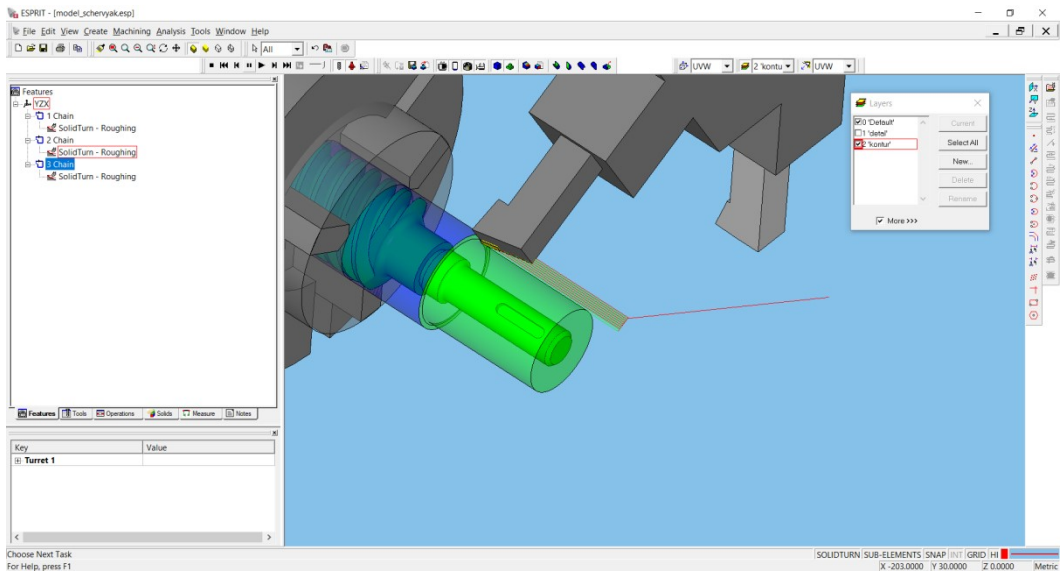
Рух металорізального інструменту траєкторією при обробленні контуру корпусу
